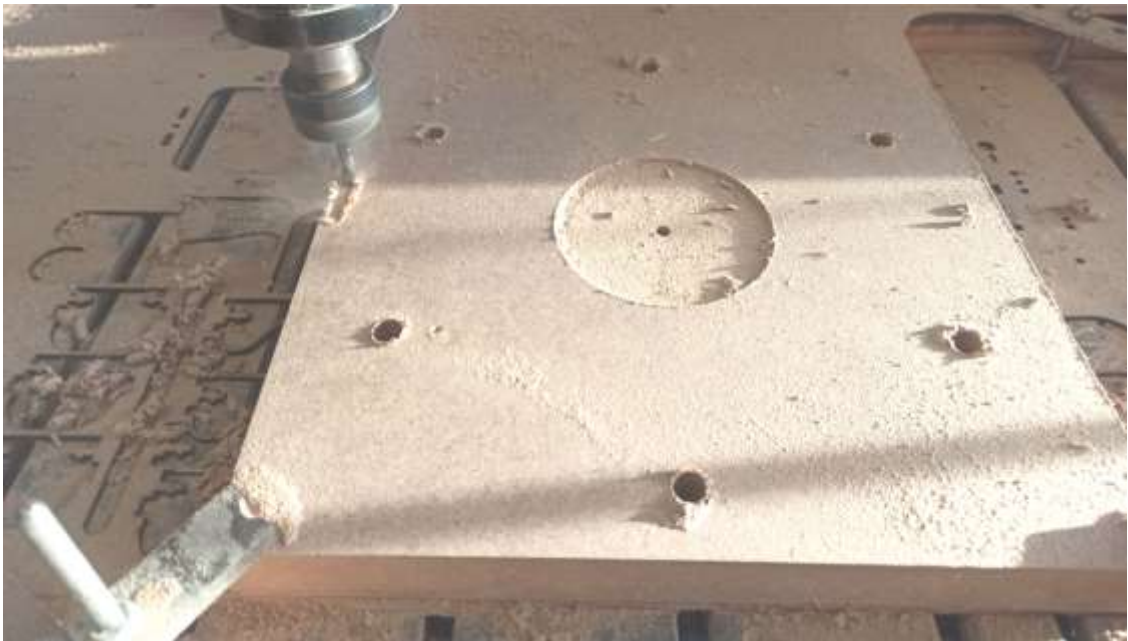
Процес фрезерування проміжного етапу виготовлення другої половини деталі типу платформа
